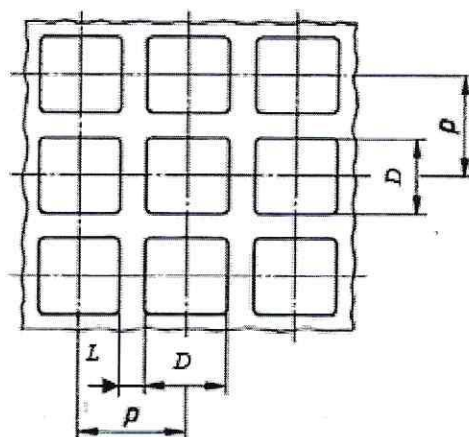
Сито с просеивающей поверхностью из перфорированной металлической пластины с квадратными отверстиями
